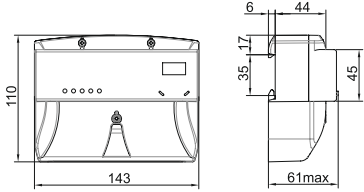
Габаритные и присоединительные размеры счётчиков габарита корпуса 6
